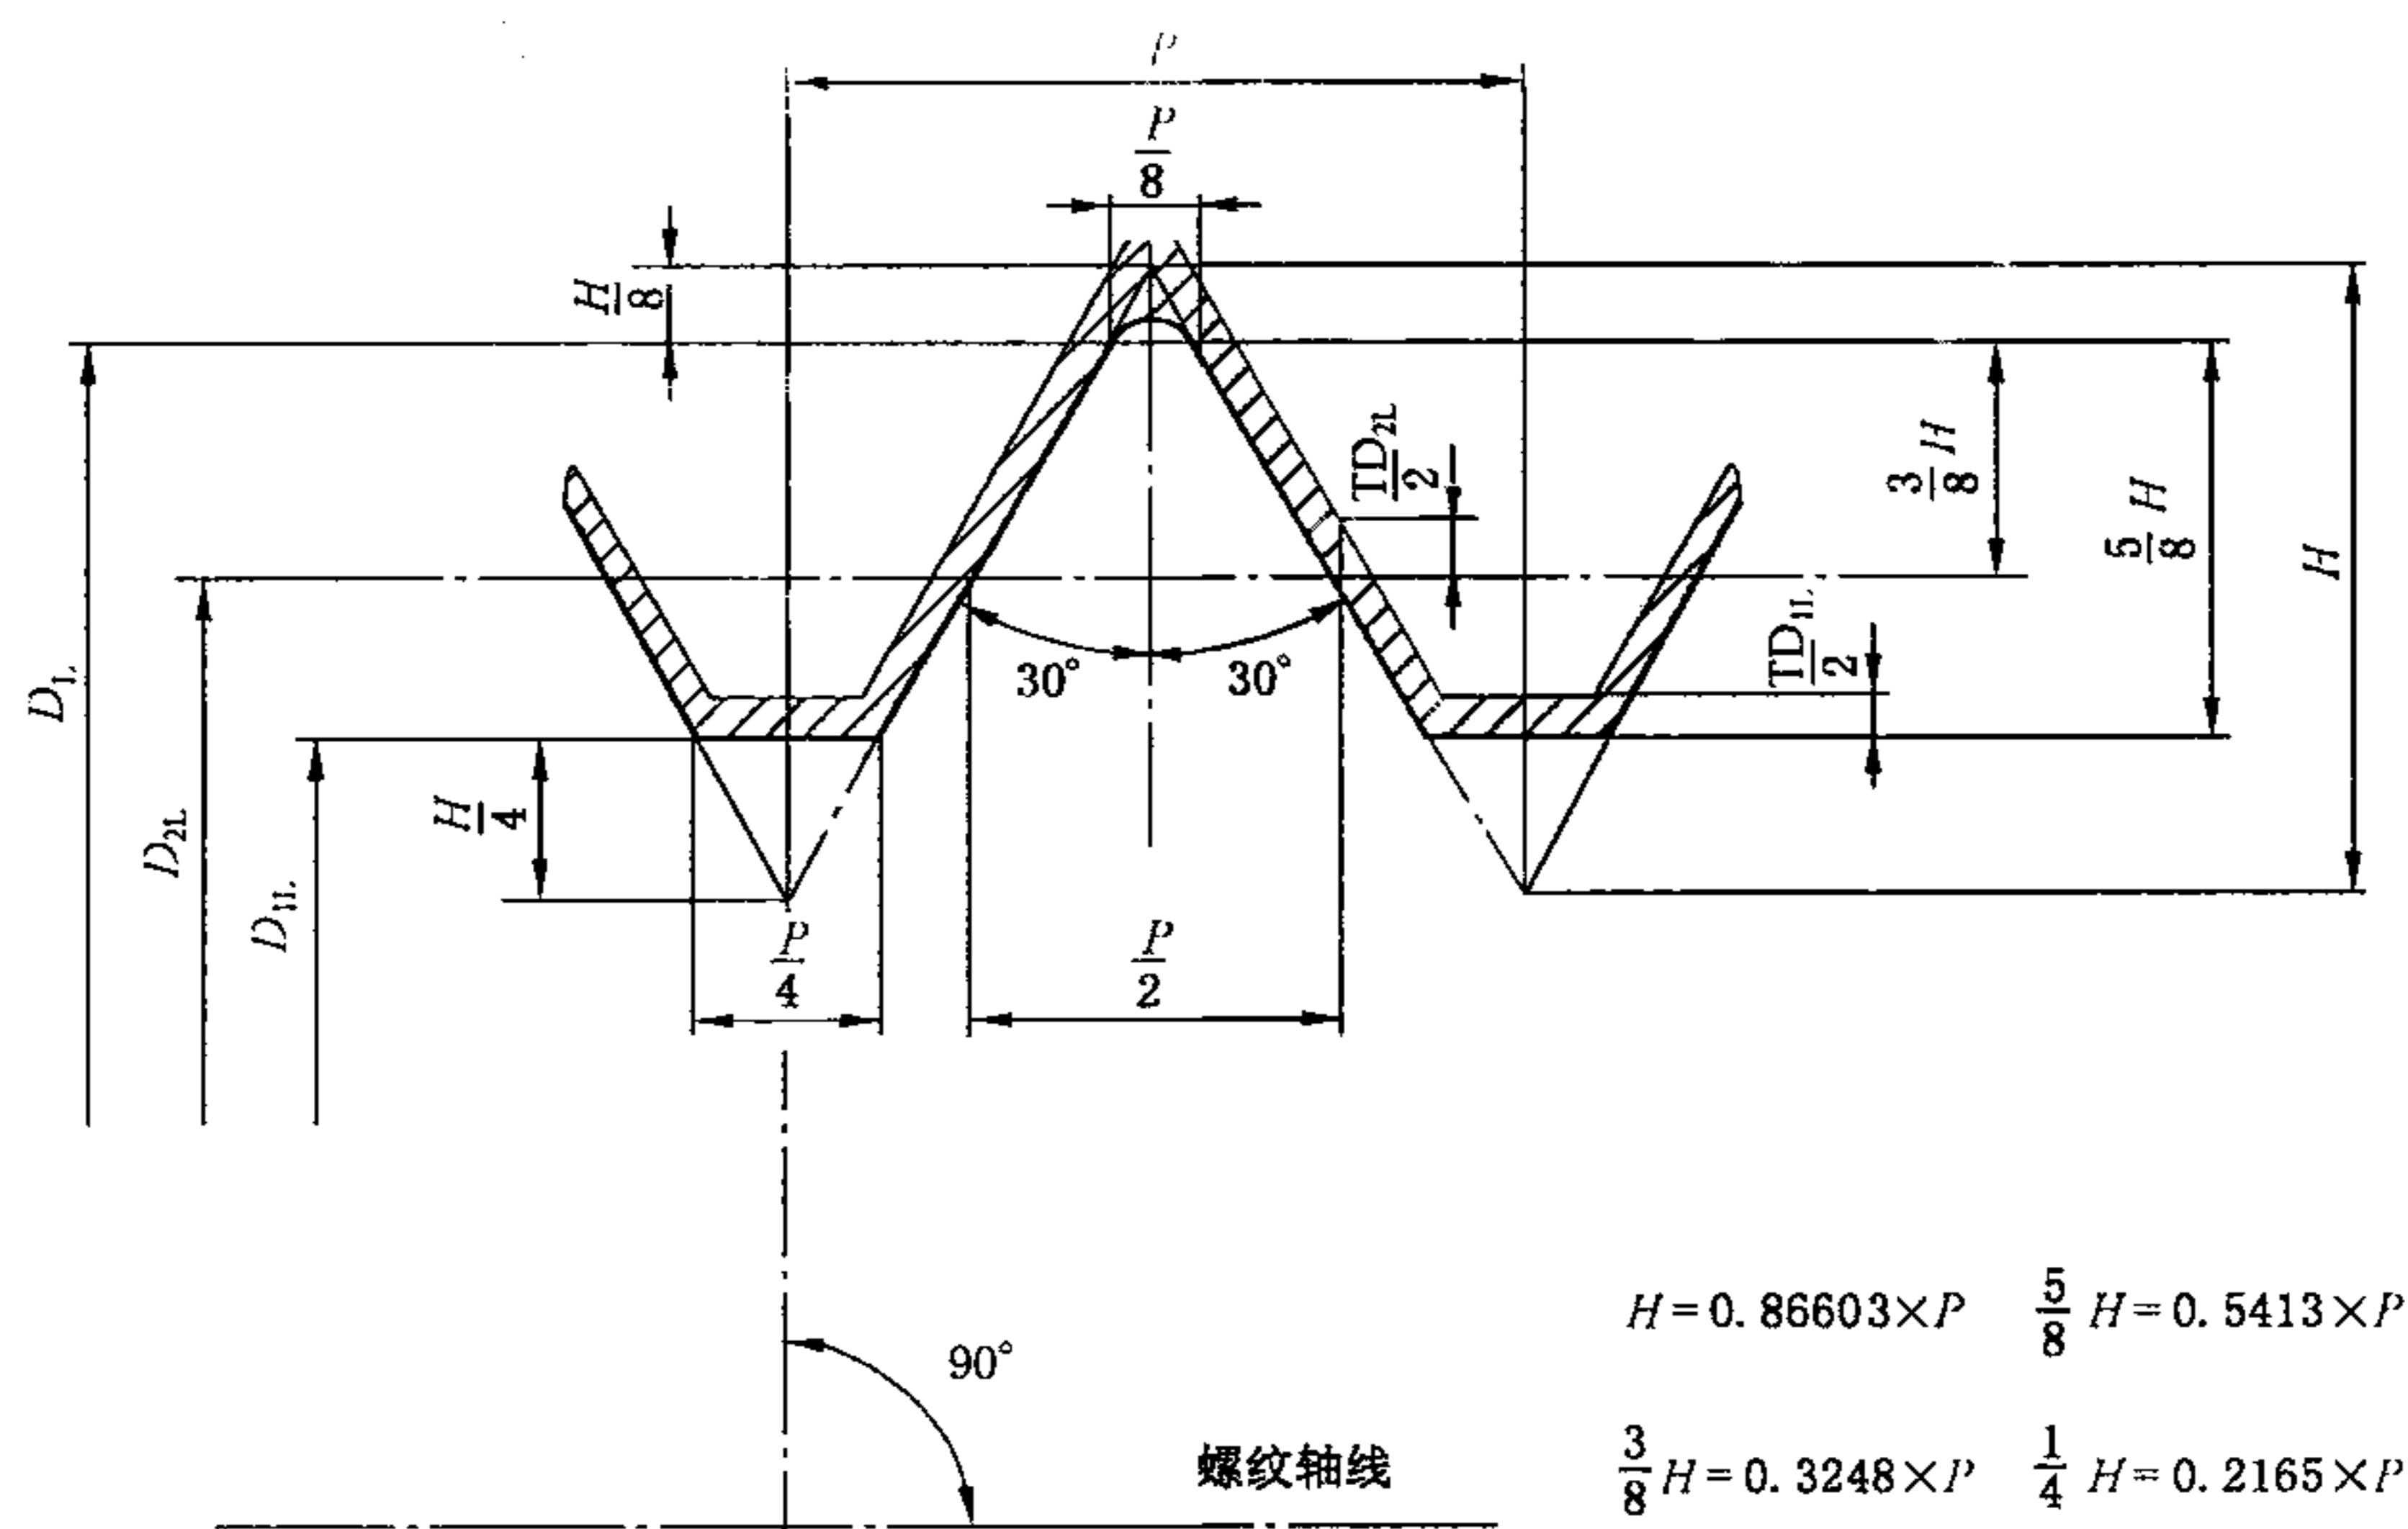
钢丝螺套用内螺纹基本牙型和公差带位置
